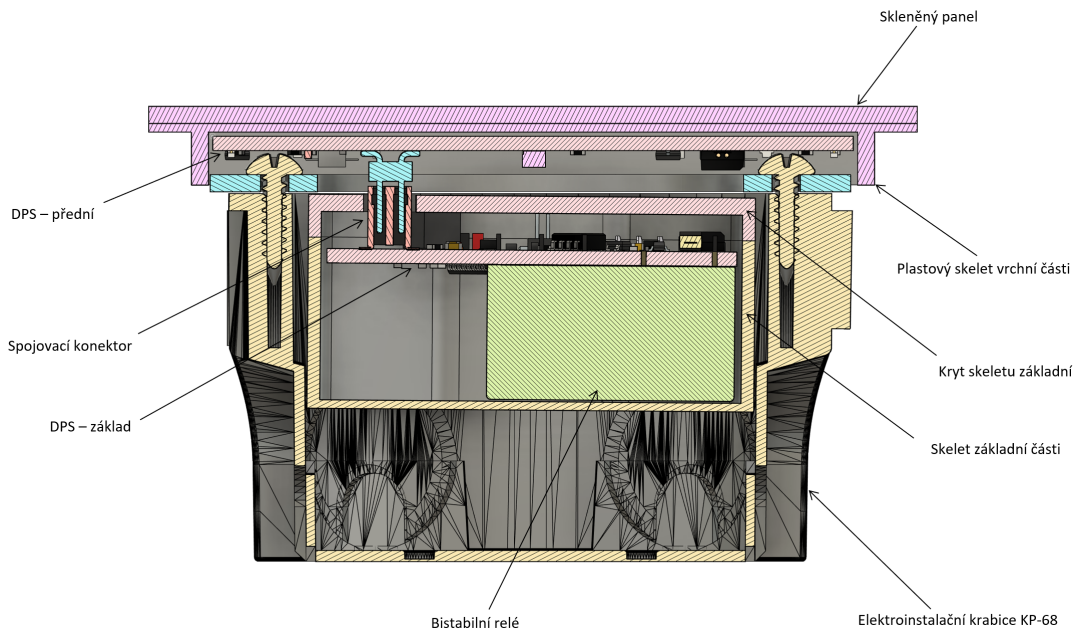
Návrh designu tlačítka (Fusion 360)
